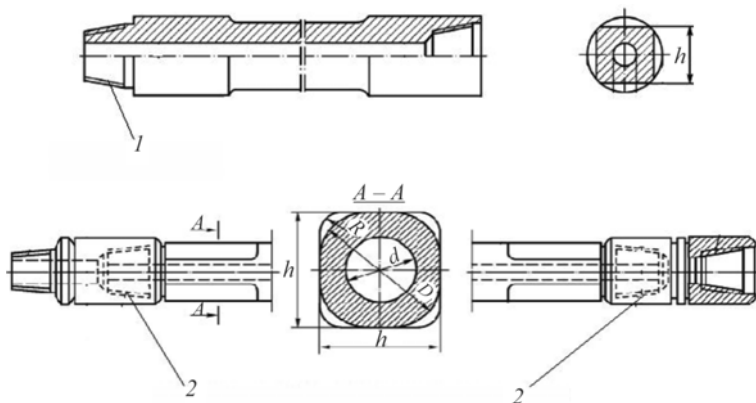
Виды аварий с ведущими бурильными трубами и УБТ: 1 – слом по коническим резьбовым соединениям; 2 – слом трубной резьбы (пятый–шестой витки от торца ведущей трубы)
